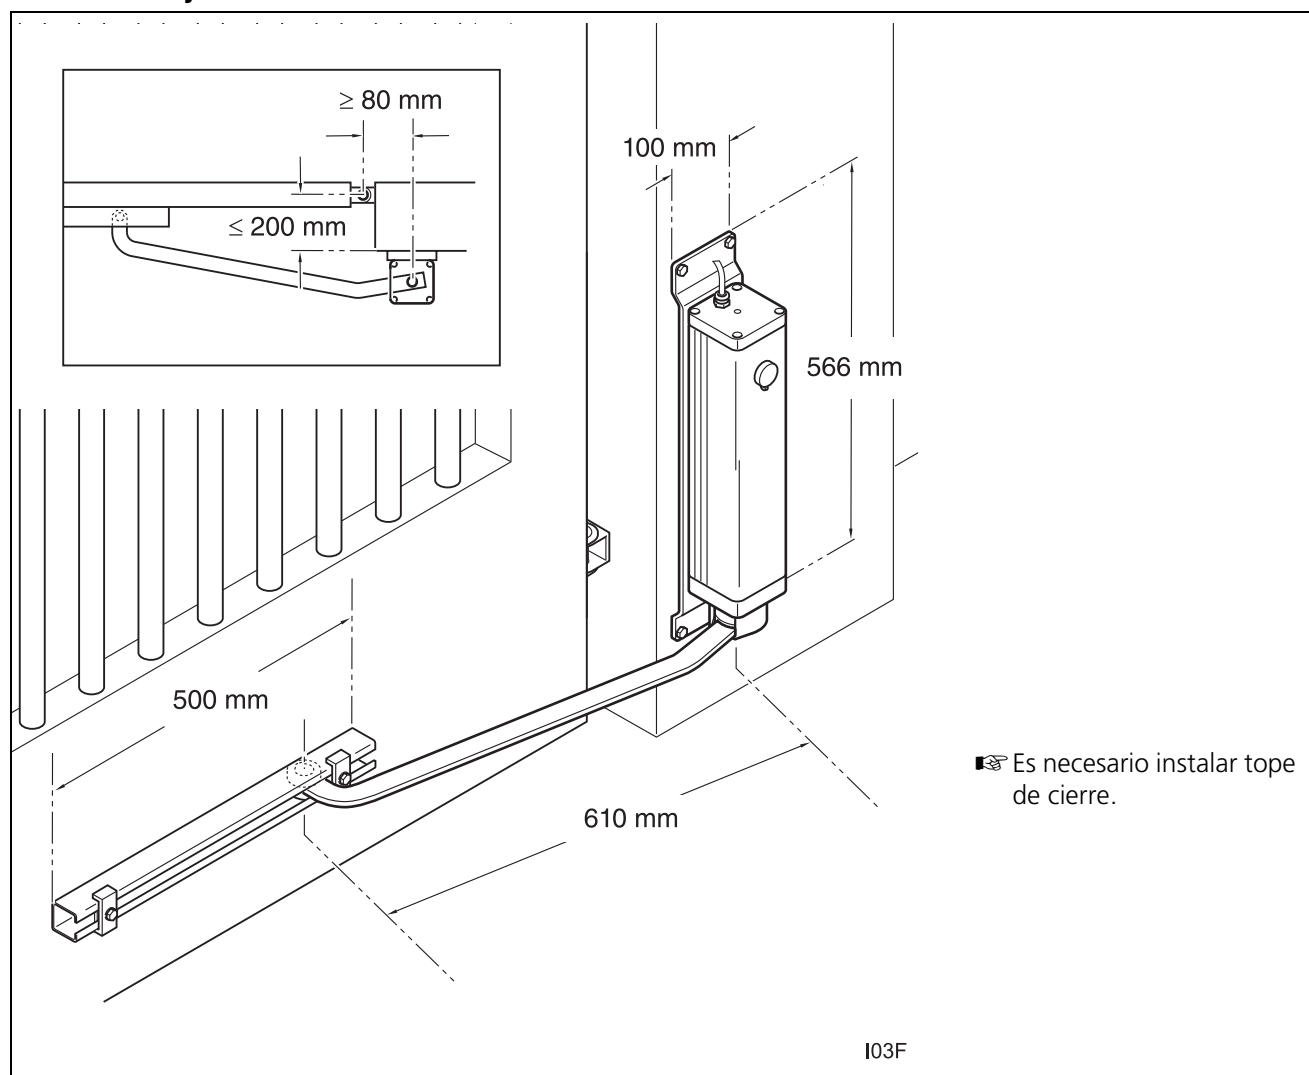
Ejemplo de posición de montaje de accionador con brazo de corredra
